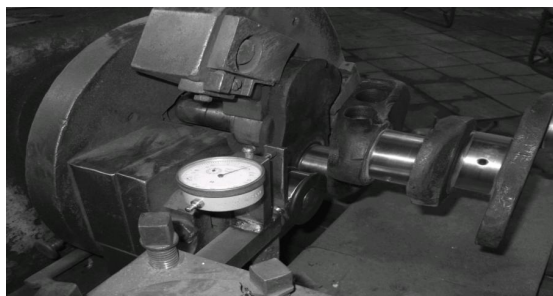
Приспособление для обкатывания галтелей на шатунных шейках коленчатого вала
